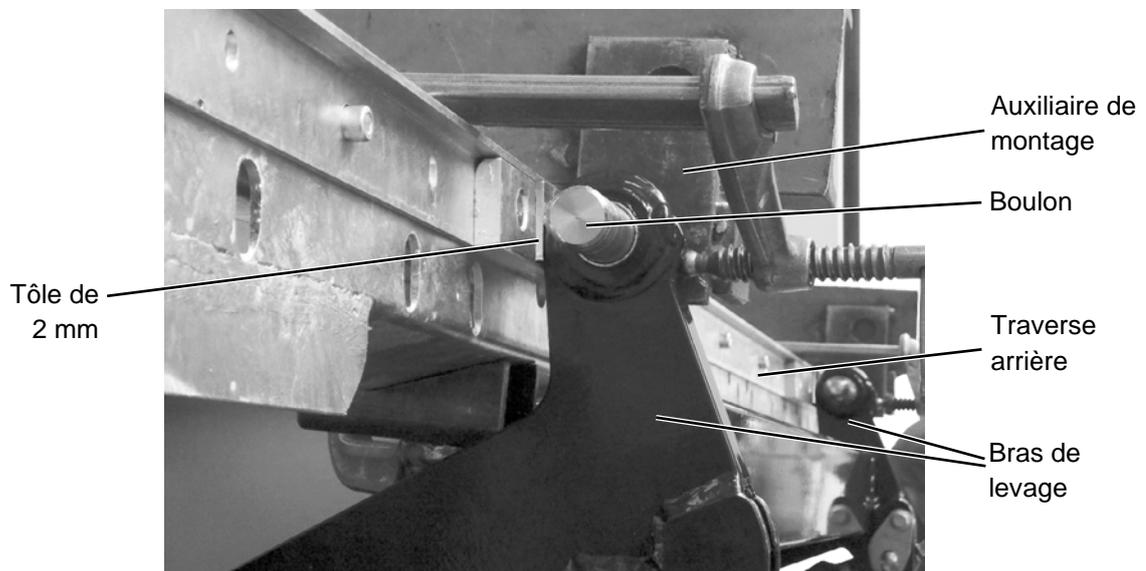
Plaques d'écartement de 2 mm lors du montage d'une plate-forme à revêtement
